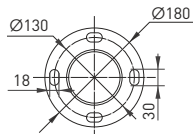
Чертеж и габаритные размеры фланца OXOR-OK2-D100
